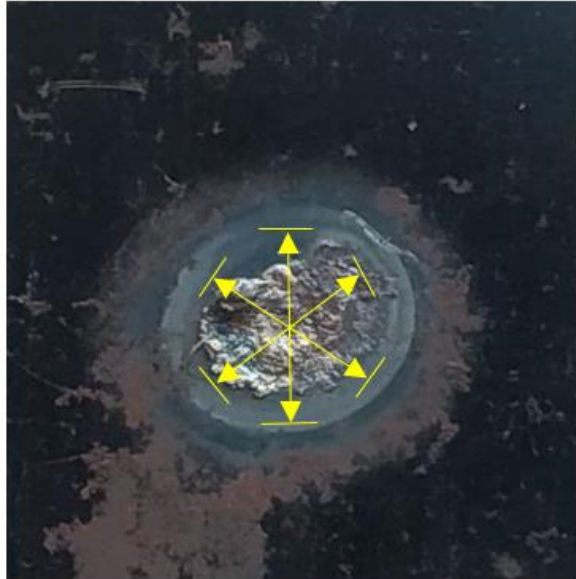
Hasil percobaan pengelasan RSW (*resistance spot welding*)
